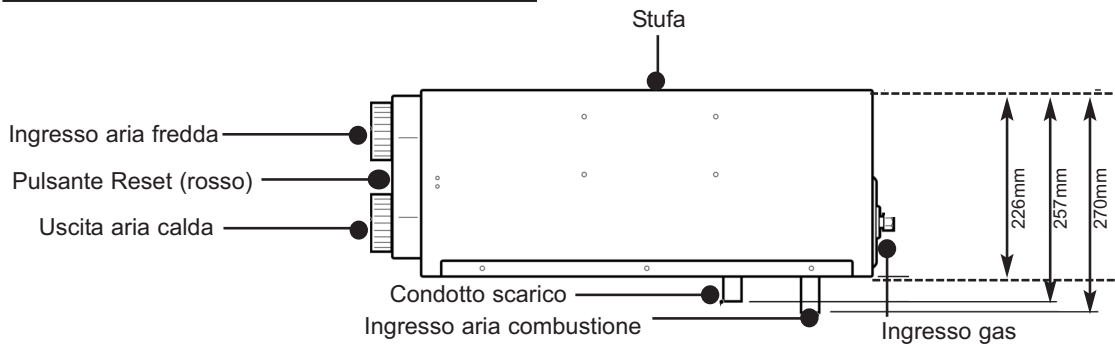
Installazione all'interno – Vista laterale - SH2201 o SC2201
